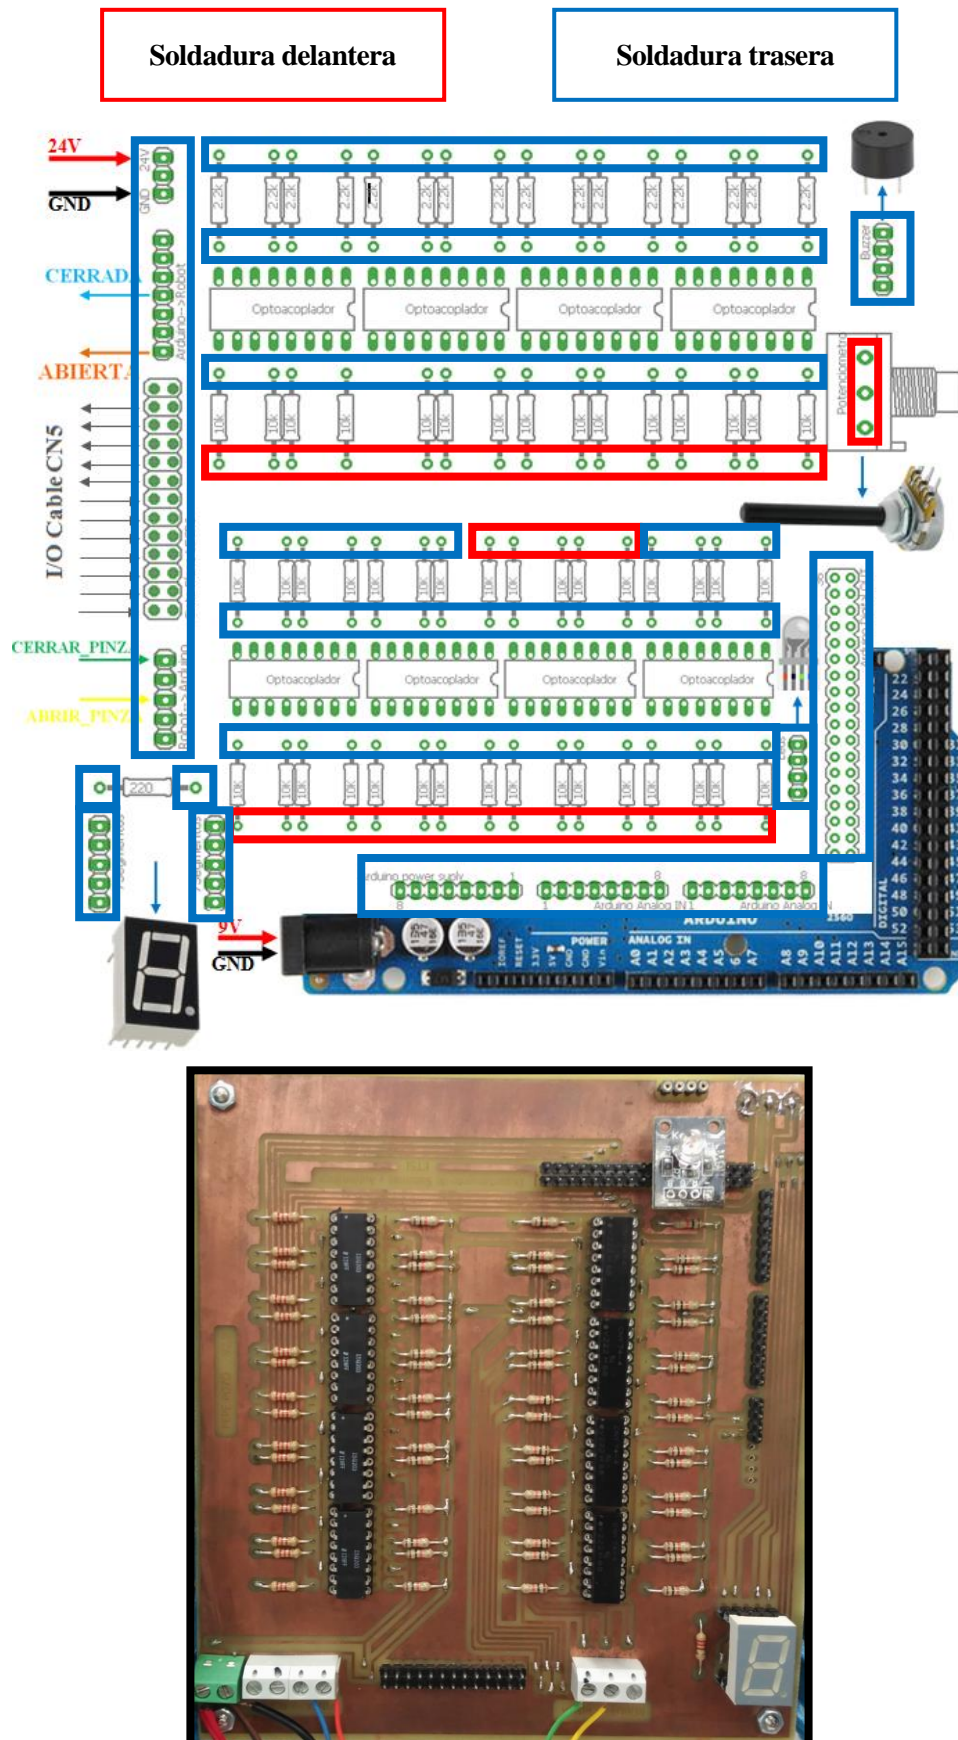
Soldaduras delanteras y traseras de la PCB
